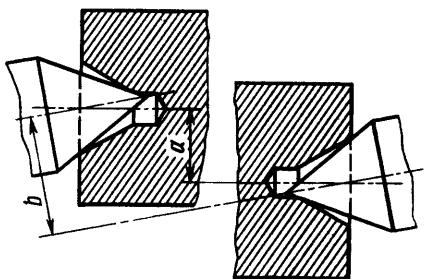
Базирование заготовки при несоосности ее центровых отверстий и центров станка
